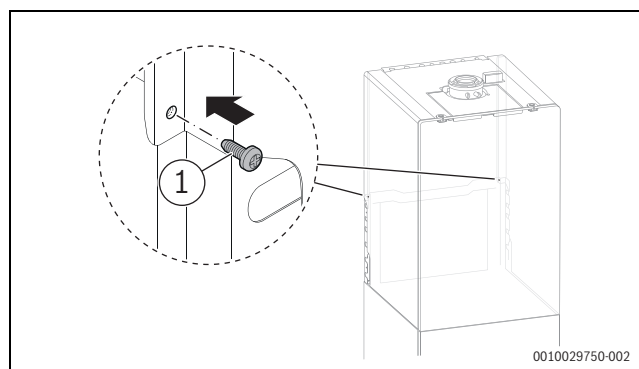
Zajištění předního panelu opláštění šroubem z rozsahu dodávky
